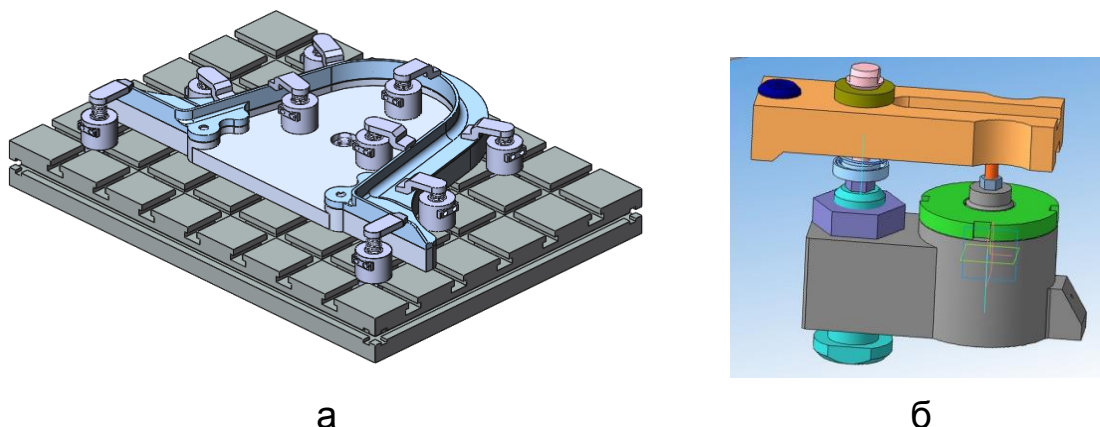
Компонування комплекту елементів УСПМ-12 для фрезерування: а – загальний вигляд; б – прихоплювач гідравлічний
